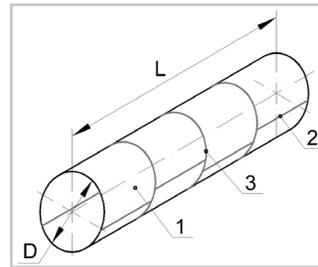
Схема сварной обечайки котла железнодорожной вагоноцистерны, сваренной из царг (коротких обечаек): 1 – царга; 2 – продольный сварной шов царги; 3 – кольцевой сварной шов обечайки; D – внутренний диаметр обечайки; L – длина обечайки
